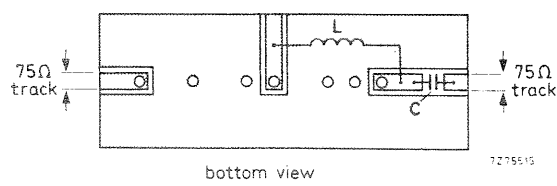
(a): - Dimensioni d'ingombro in un modulo OM 336.
